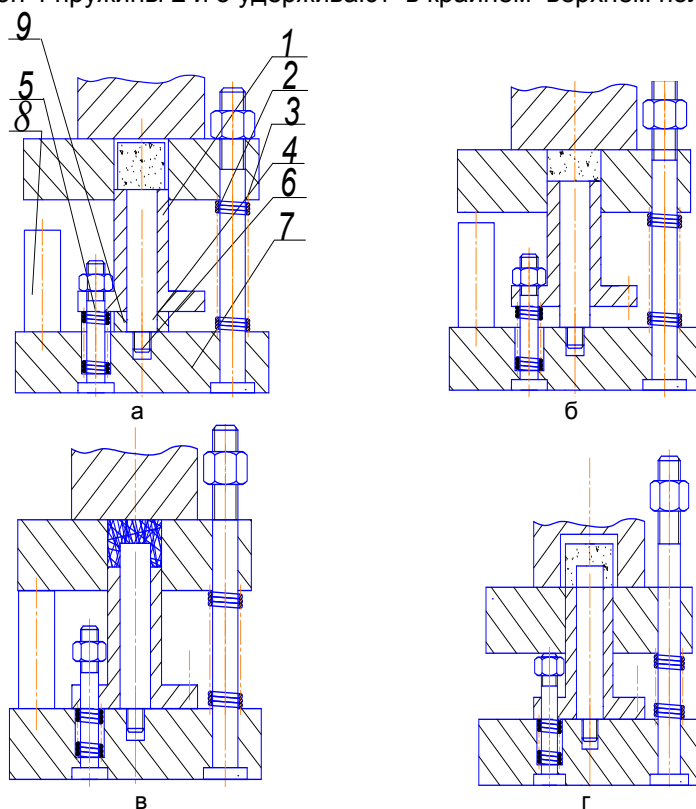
Схема штампа для выдавливания полых порошковых деталей:
